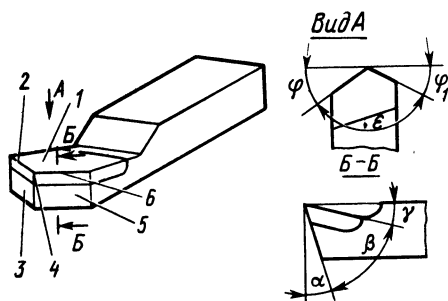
Расточный резец с напайной твердосплавной пластиной
